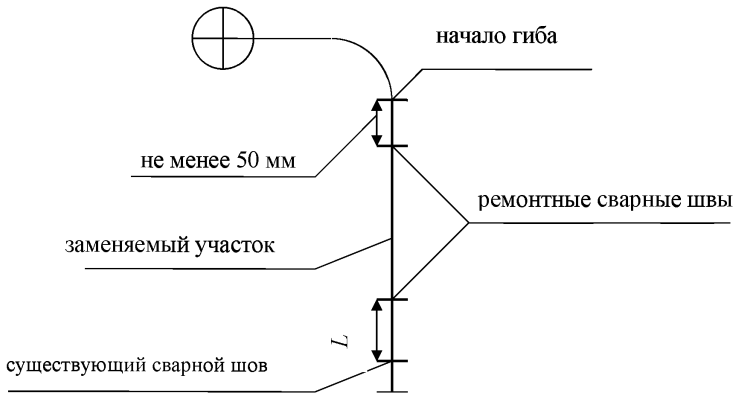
Расположение ремонтных сварных швов
